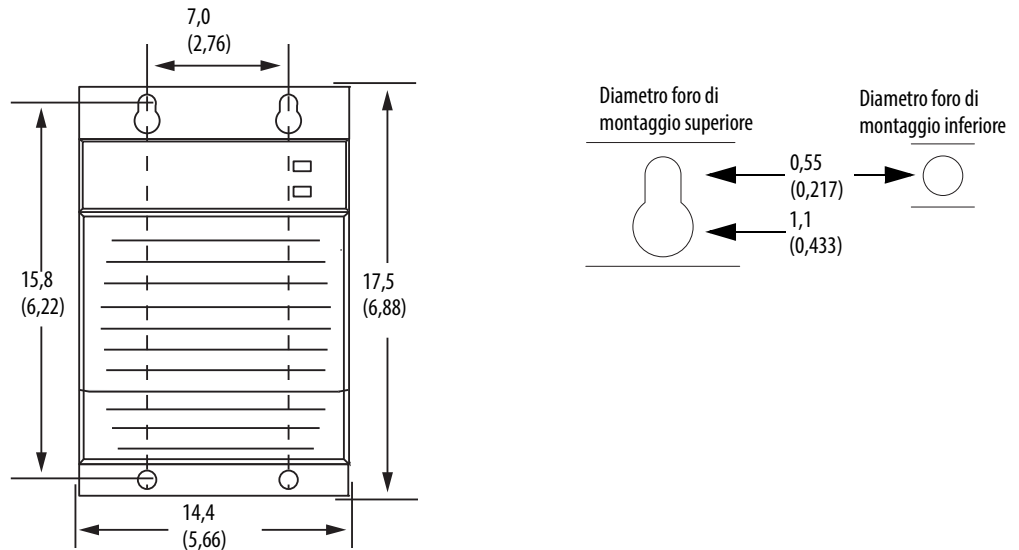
Dimensioni comuni degli chassis (Serie C)
